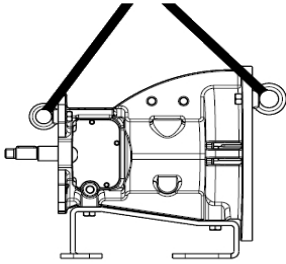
Lagerlaterne A / *Illustration 11: Bearing lantern A
